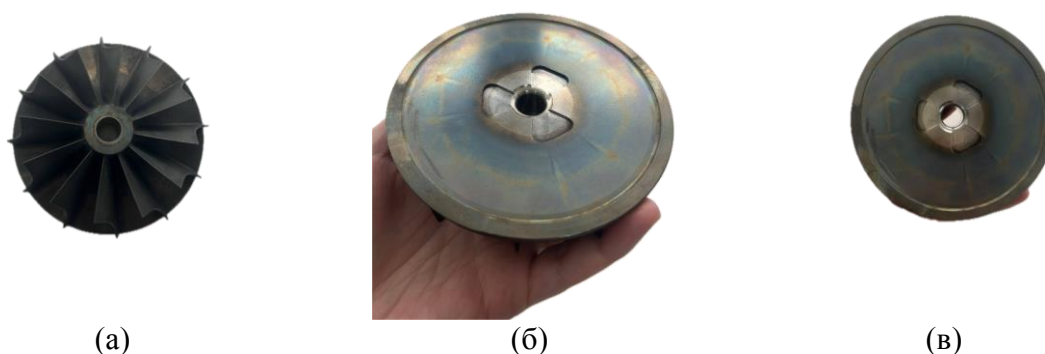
Макрофотографии заготовки «Крыльчатка турбины» после натуральных испытаний: (а) вид со стороны лопаточного венца, (б, в) обратная торцевая поверхность колеса турбины с радиальными следами, визуально напоминающими трещины
